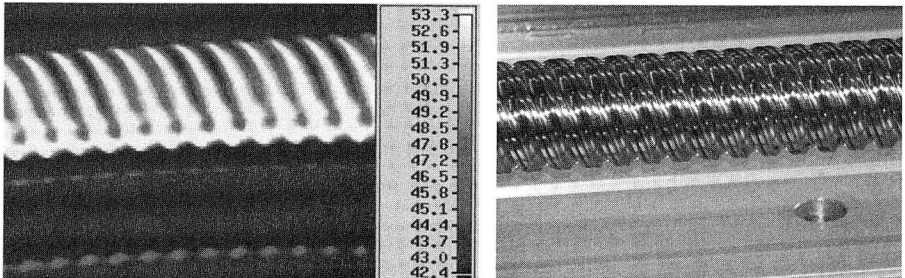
Kugelgewindetrieb: Aufnahme mit Thermokamera (links) und Bildaufnahme (rechts)
